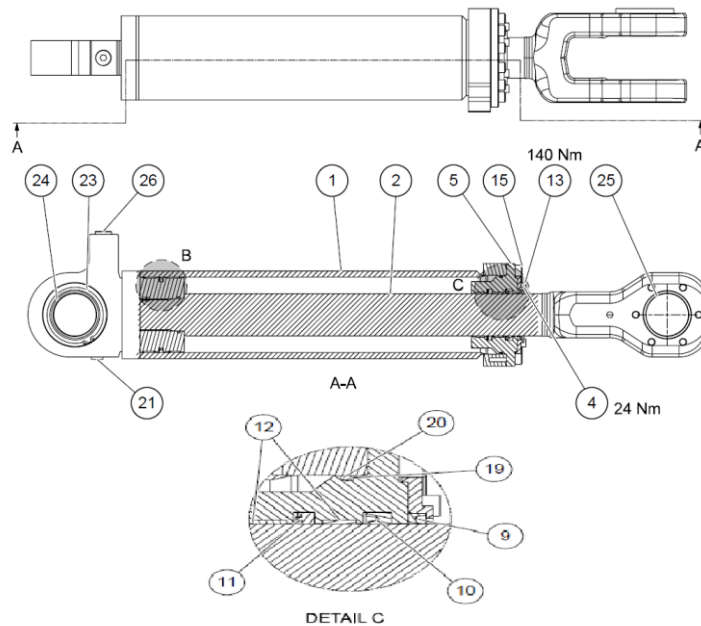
Эскизный чертеж ПДМ Sandvik LH514 гидроцилиндра
